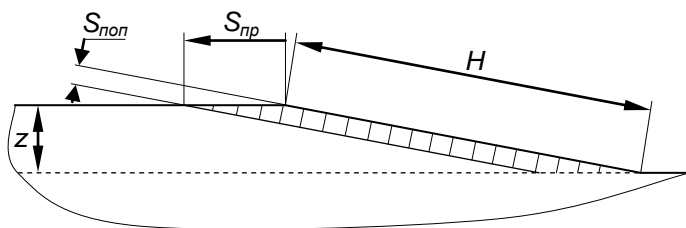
Схема съема припуска при бесцентровом шлифовании со скрещивающимися осями инструмента и детали
